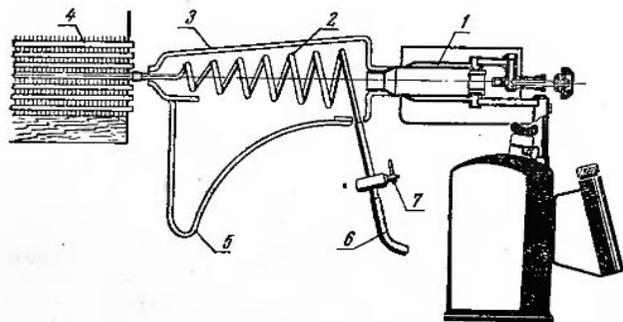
Паяльная лампа для отпайки трубок от пластин: 1 — горелка; 2 — змеевик; 3 — кожух; 4 — сердцевина радиатора; 5 — подерживающий упор; 6 — шланг для подачи сжатого воздуха; 7 — кран.
